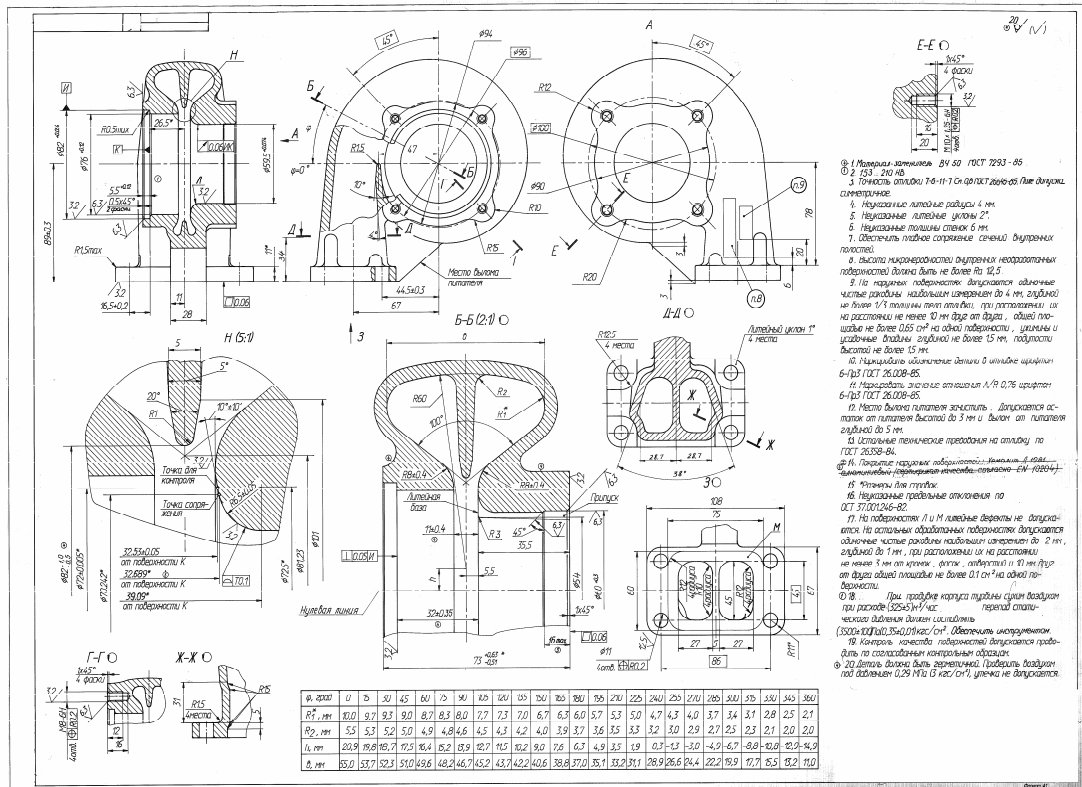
Чертеж детали корпуса турбины турбокомпрессора
